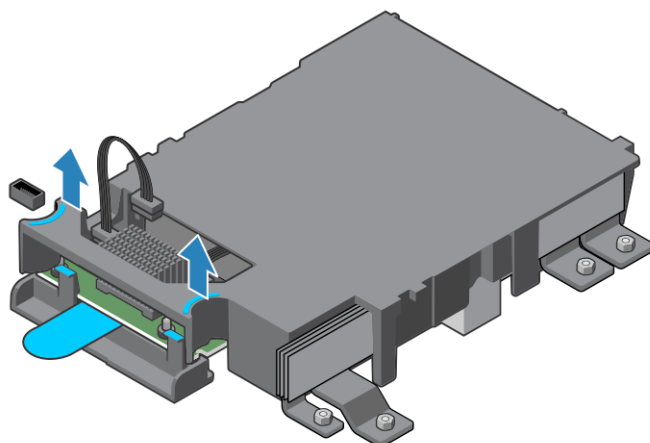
Extracción de la cubierta del Módulo de batería de reserva interna de la placa base
